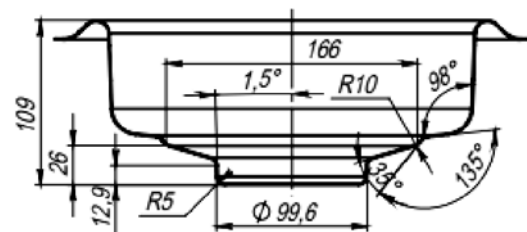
Ескіз напівфабрикату корпусу вентилятора
